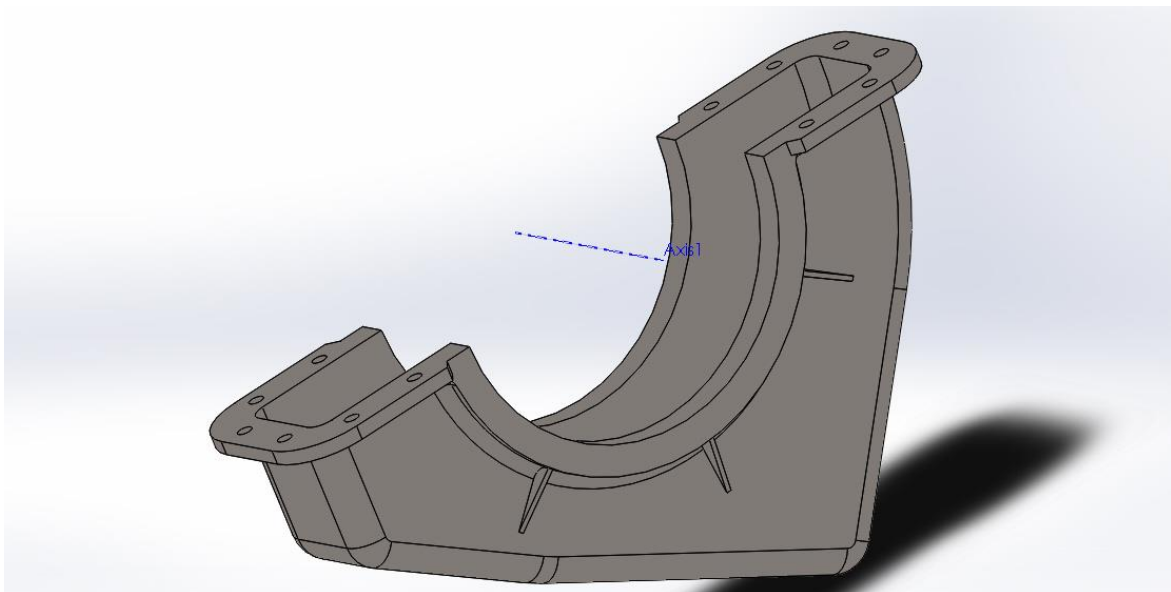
3D модель деталі "Корпус нижній"
